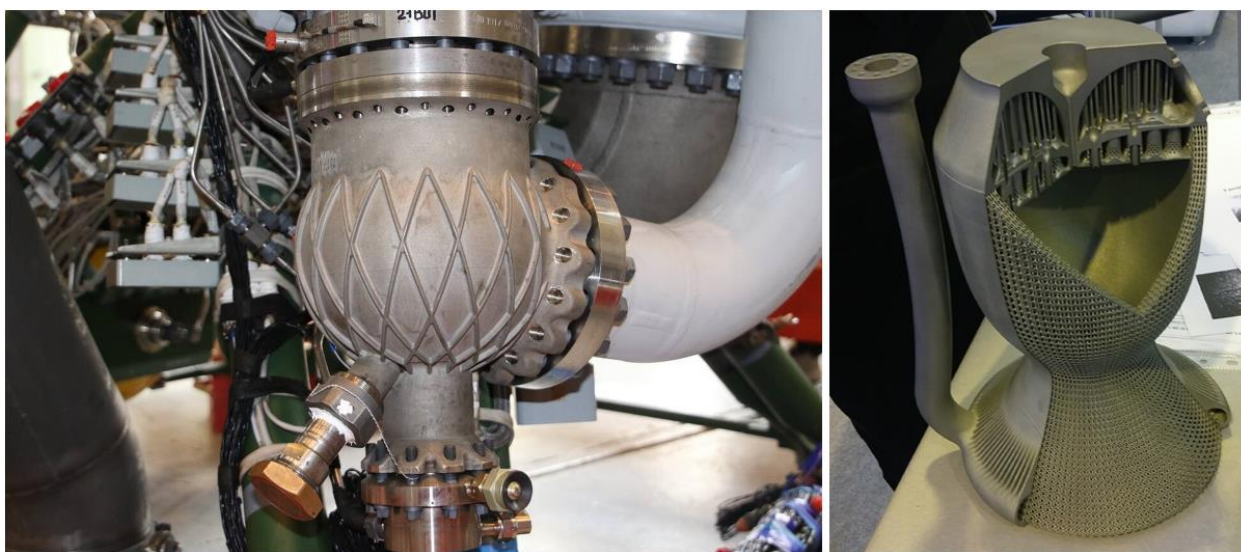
Ракетный двигатель для ракеты носителя «Ангара» (слева), Жидкостной ракетный двигатель(справа), напечатанные их металлического порошка
